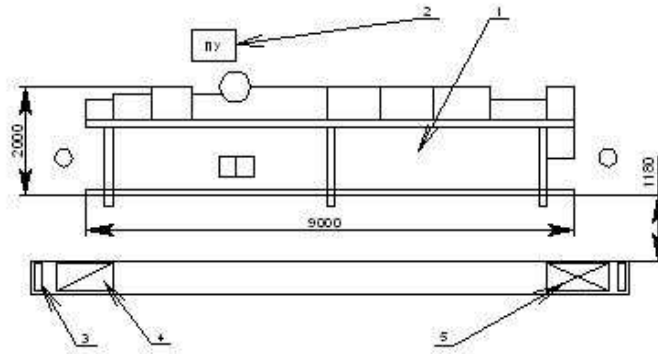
Станок односторонний облицовки прямых и профильных кромок Нотаг
